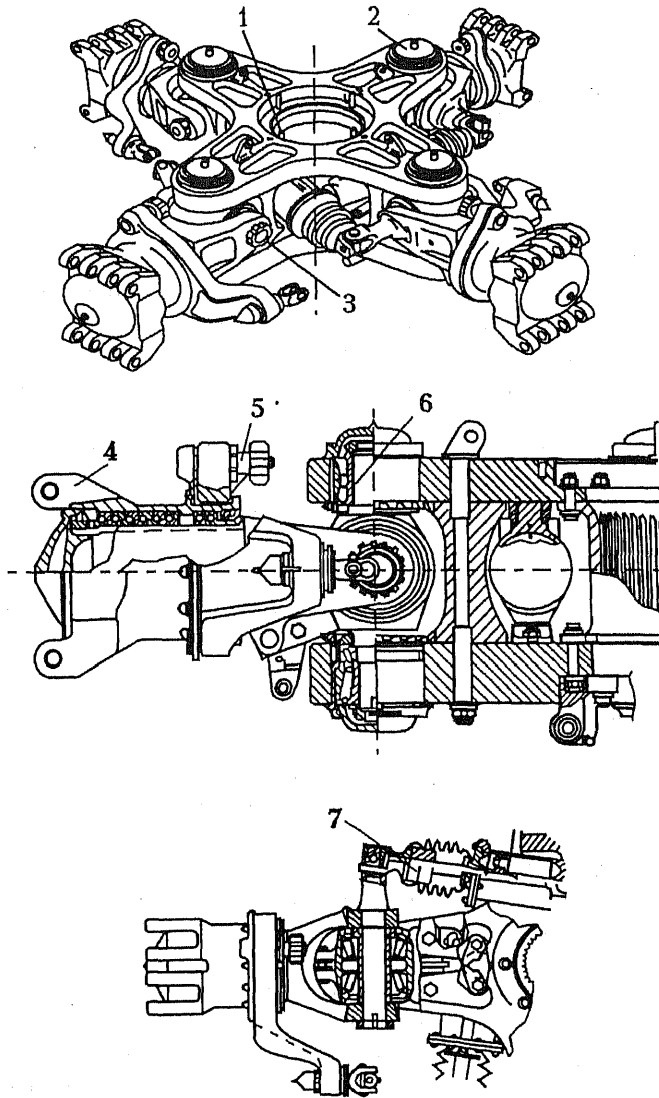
Конструктивно-кинематическая схема шарнирной втулки с совмещенными ГШ и ВШ:
